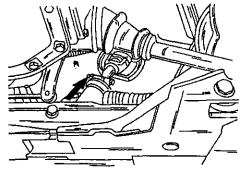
Стрелкой указан стяжной болт крепления рулевого вала к шестерне.
